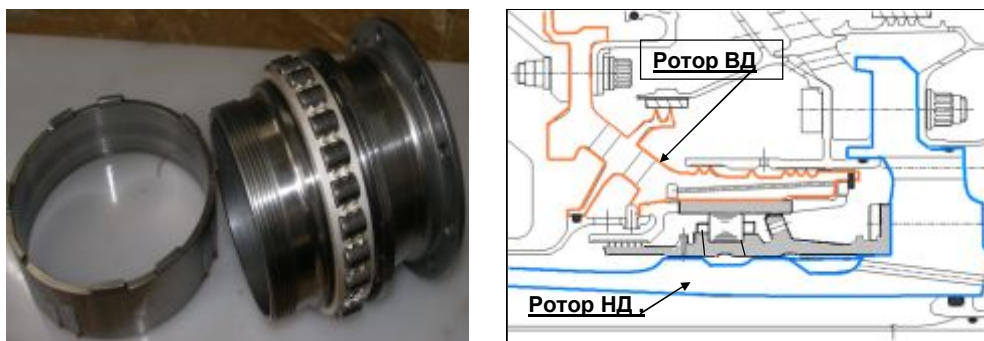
Конструкция межроторного подшипника фирмы SKF для двигателей CFM-56 и SaM-146
